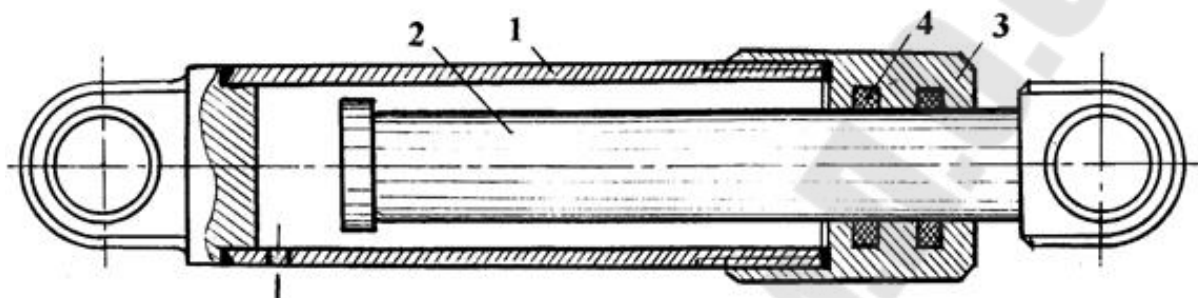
Конструкция плунжерного гидроцилиндра
